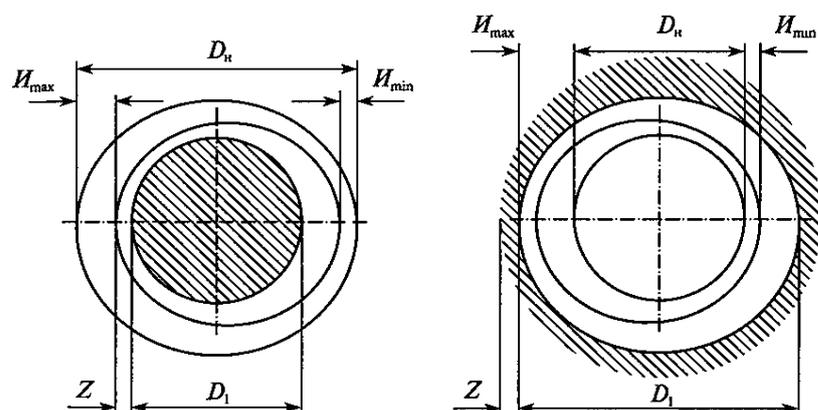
Схемы обработки вала и отверстия под ремонтный размер
